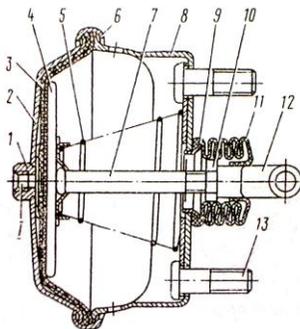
Тормозная камера передних тормозных механизмов:
